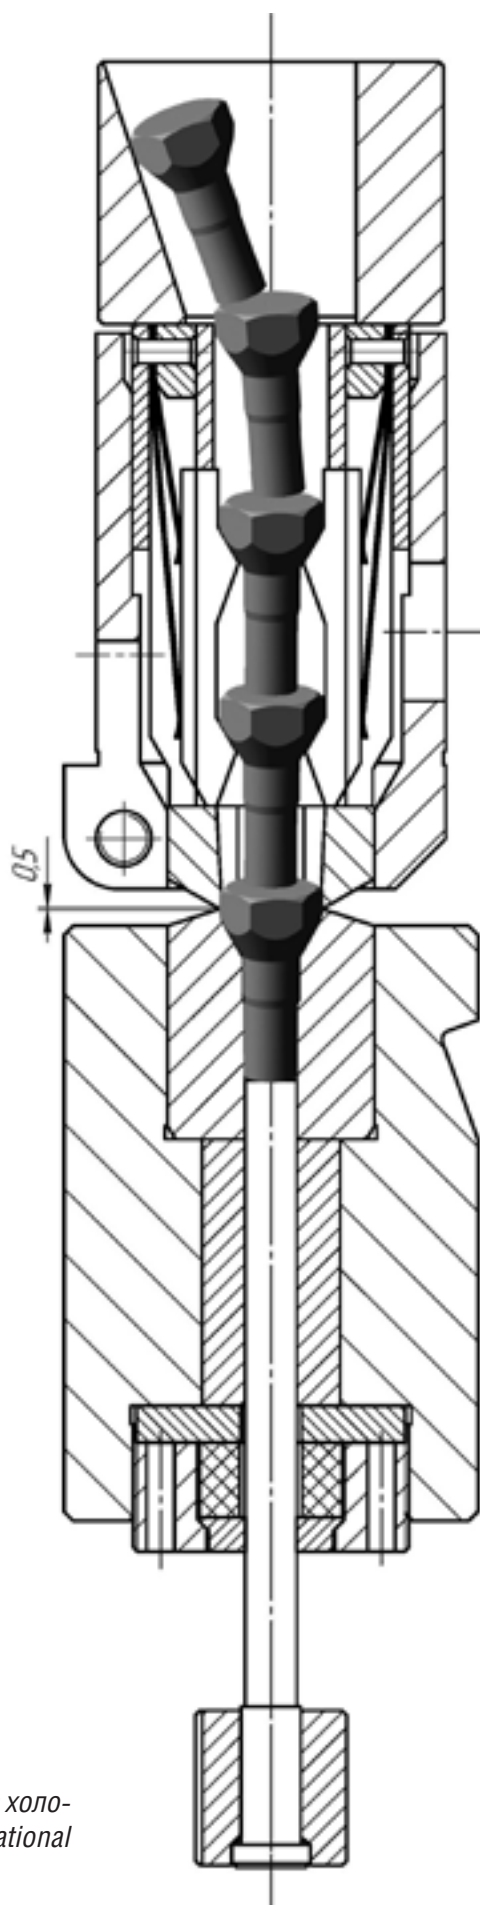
Конструкция инструмента четвёртой позиции высадки на холодновысадочном автомате 1/2" S3 4-Die Boltmaker фирмы National Machinery Co.
